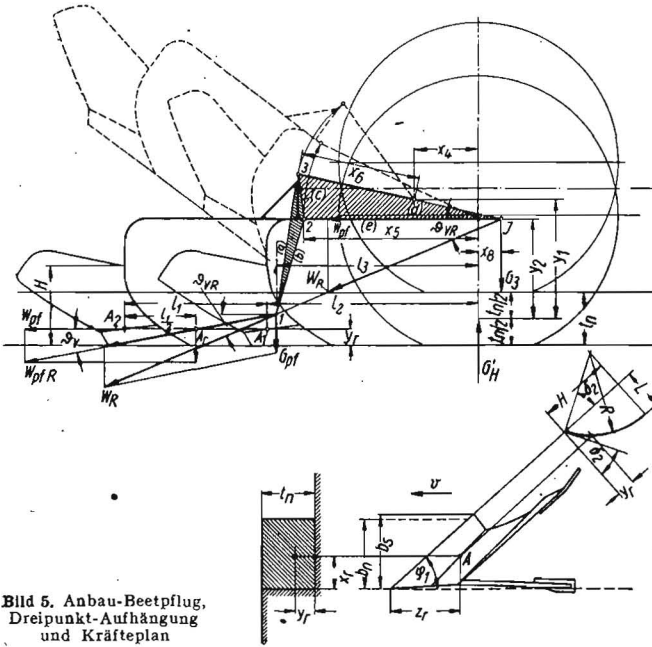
Anbau-Beetpflug, Dreipunkt-Aufhängung und Kräfteplan
